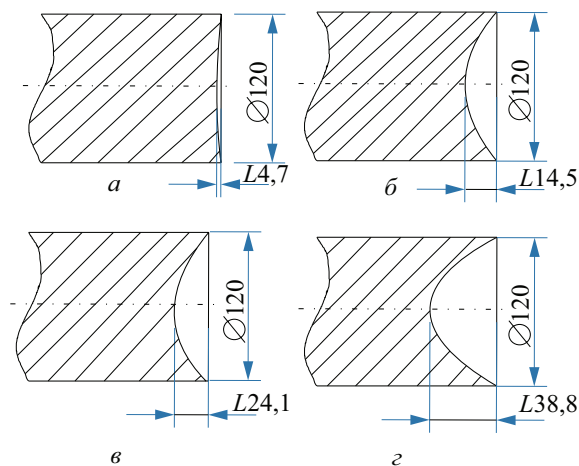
Концевая часть заготовки перед прошивкой:
